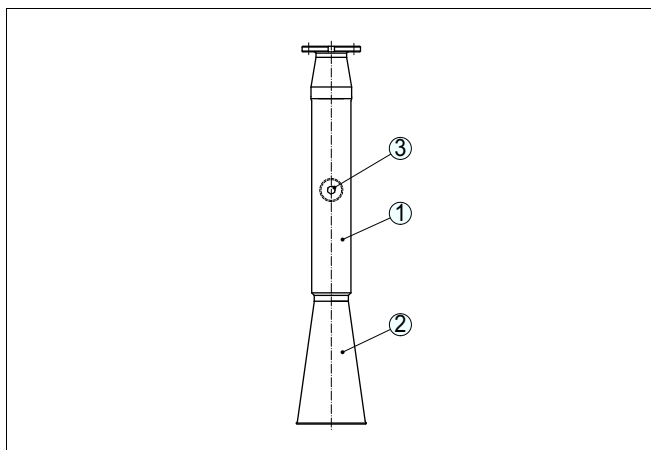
Prolongamento reto de um segmento com antena tipo corneta soldada
